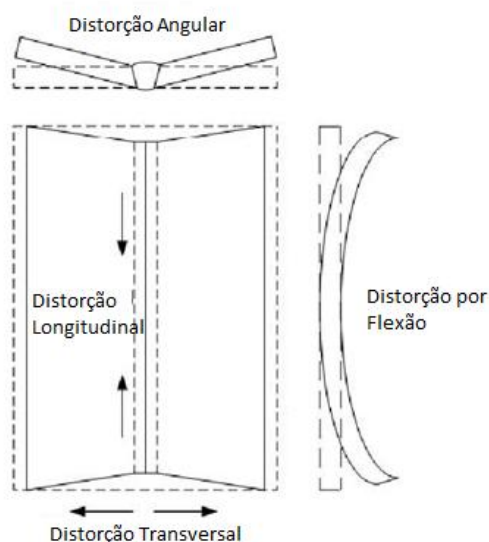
Exemplos básicos de distorções em uma chapa soldada [3]
